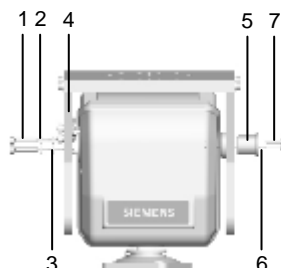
Austausch der Plattform für Aufsatzmontage durch eine Halterung für seitliche Montage
